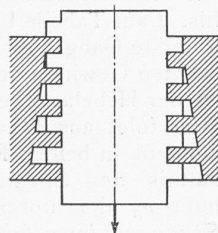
Hinterdrehtes Gewinde nach Solt.
